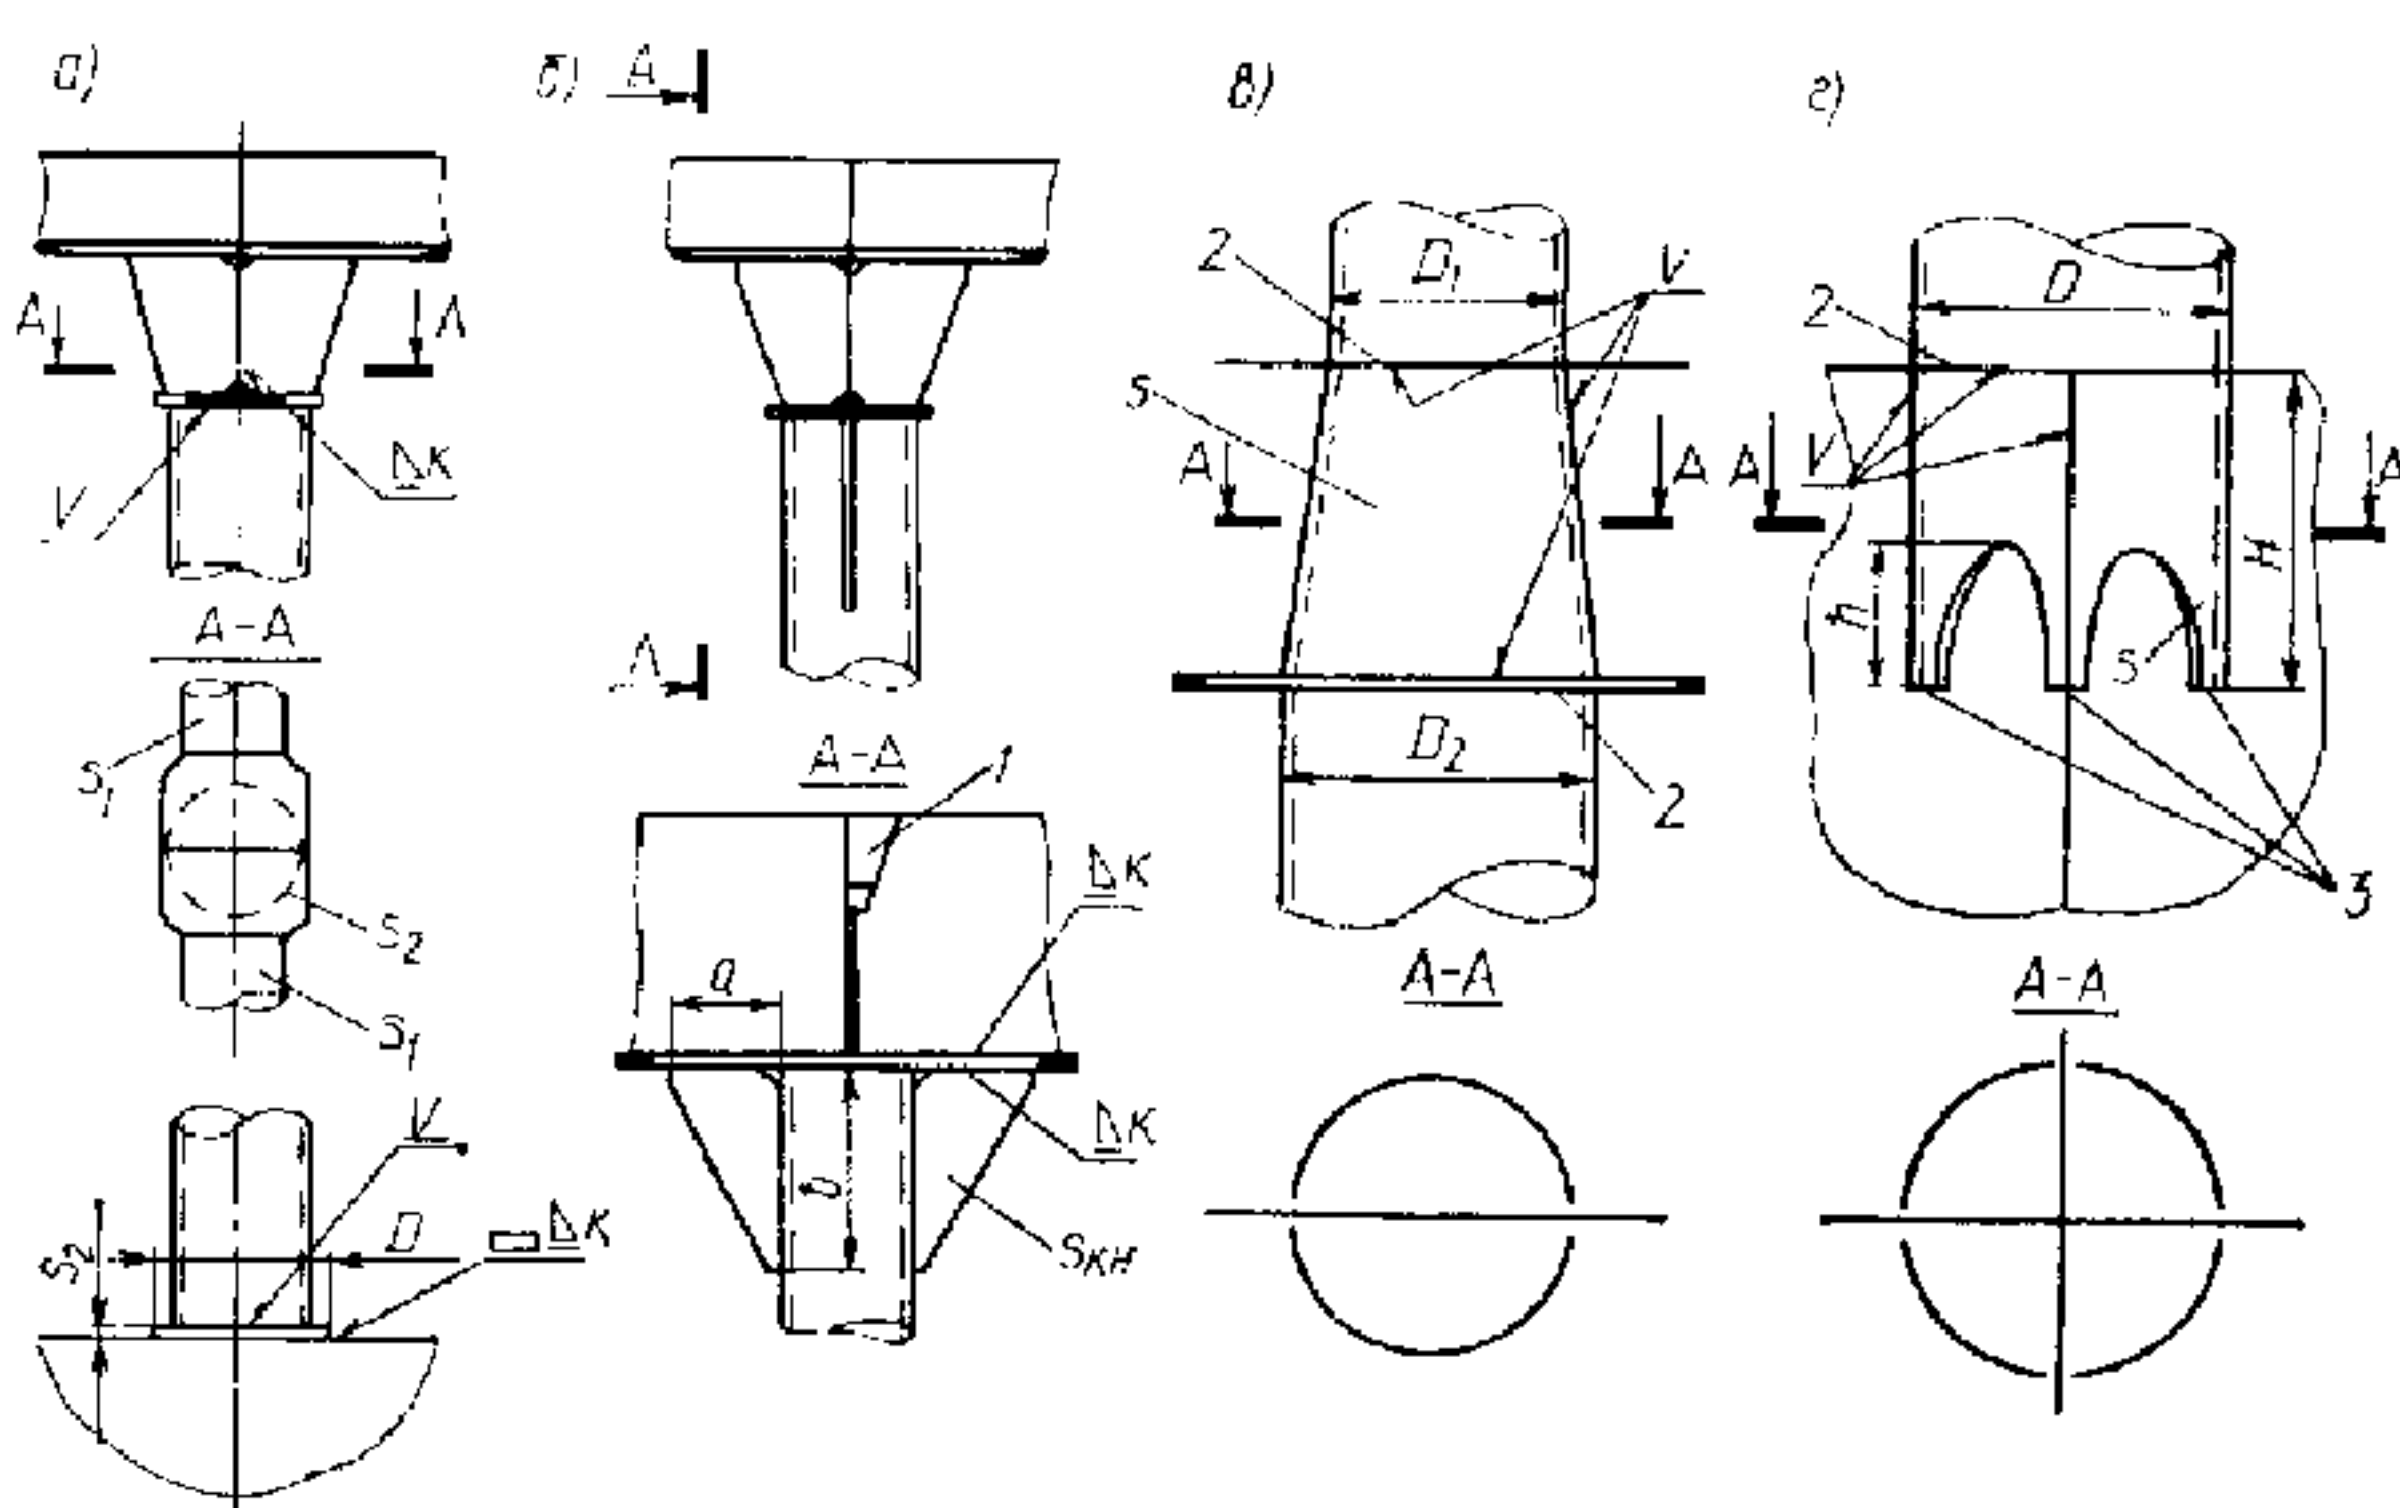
Конструкции закрепления верхних и нижних концов пиллерсов:
